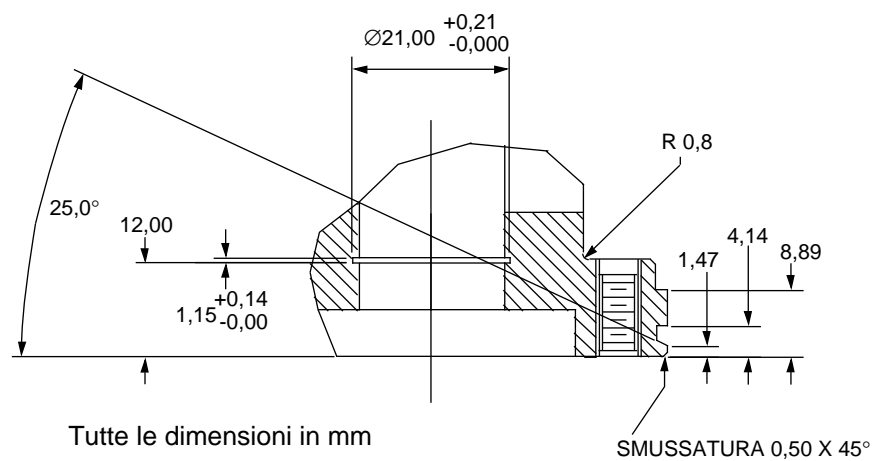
Dimensioni delle flange utente in vista ravvicinata
